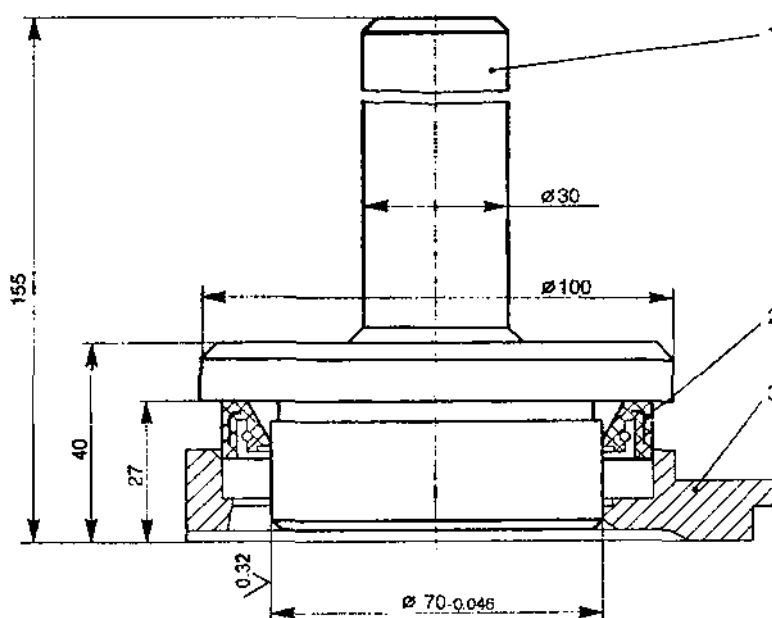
Запрессовка манжеты в держатель заднего подшипника коленчатого вала:
